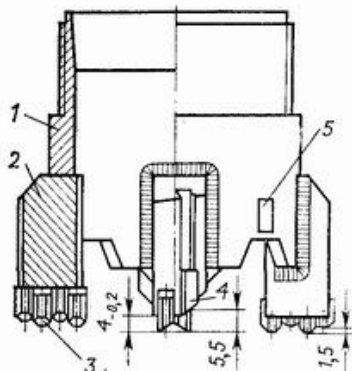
Внешний вид твердосплавной коронки CM-5:
